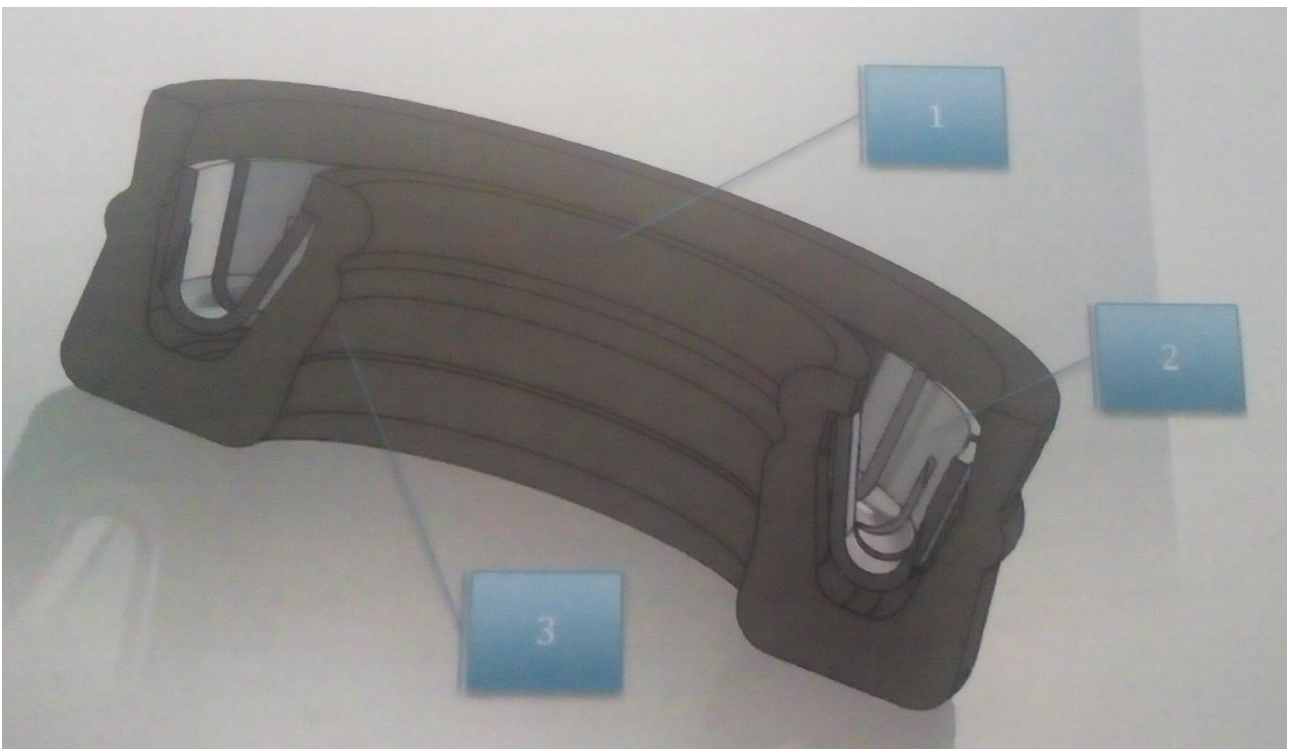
Sezione Special Rod Optiseal® - disegno di controllo ID-001653-11-00
